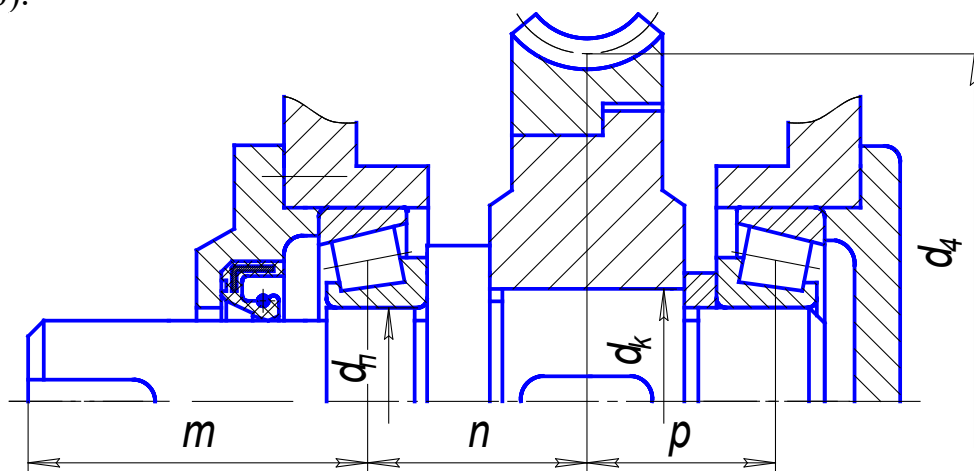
Тихоходный вал зубчато-червячного редуктора
